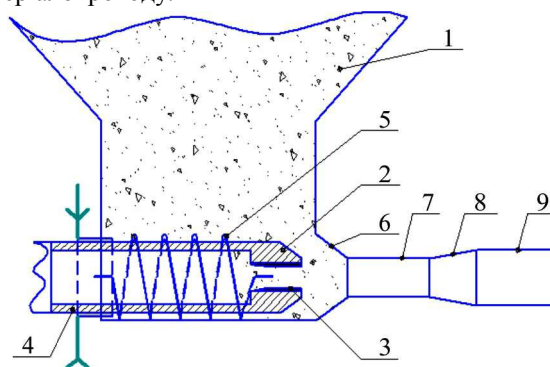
Схема ежекційної установки: 1) витратний бункер піноскла; 2) порожнистий шнековий дозатор-живильник; 3) робоче сопло шнекового дозатора-живильника; 4) приводна частина шнекового дозатора-живильника; 5) перетрушувач-живильник пружинного типу; 6) конфузур; 7) камера змішування (розгінна трубка); 8) дифузур; 9) фланець підключення рукавної лінії матеріалопроводу
